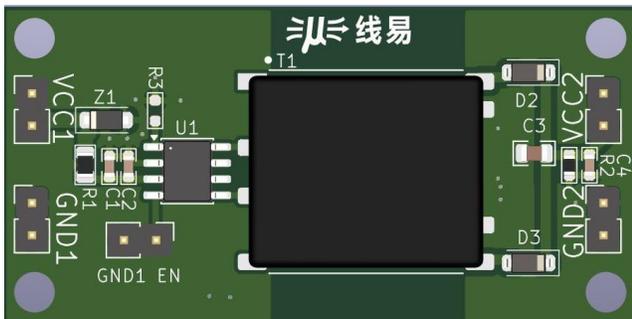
PCB 版图正面 (尺寸: 25 x 50mm)
